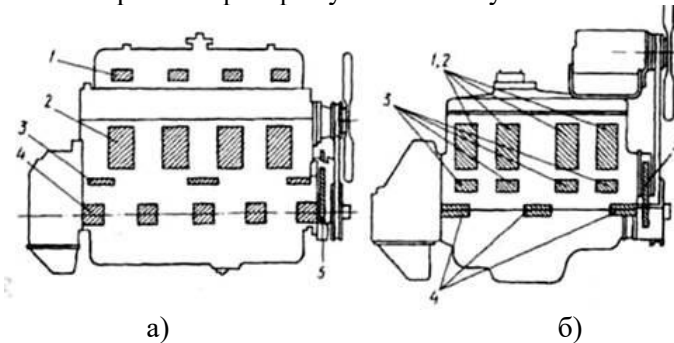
Ділянки прослуховування двигунів: а – двигун з верхніми клапанами; б – двигун з нижніми клапанами; 1 – ділянка клапанів; 2 – ділянка поршнів; 3 – ділянка штовхачів; 4 – ділянка підшипників; 5 – ділянка розподільчих шестерень (або приводу).
